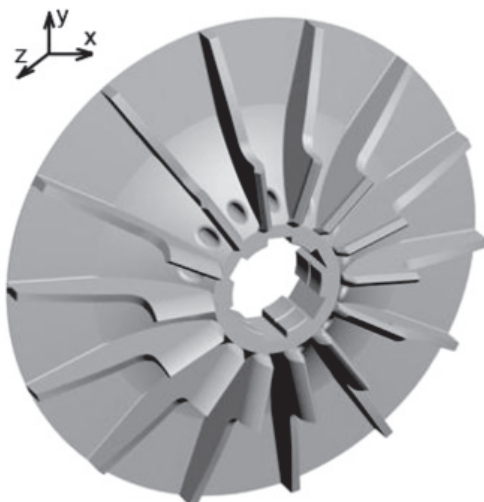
Исследуемая центробежная крыльчатка компрессора полуоткрытого типа
